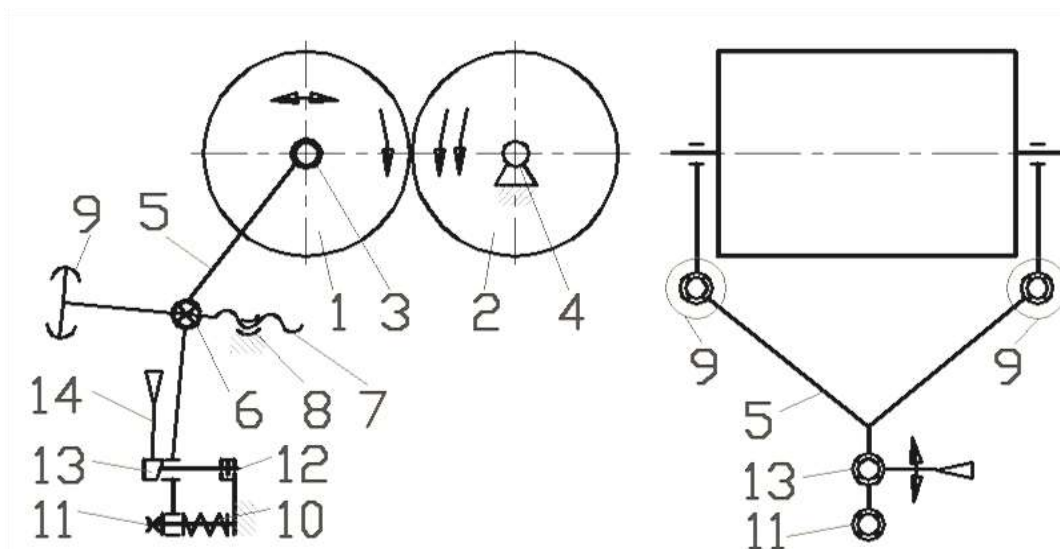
Схема установчого механізму вальцьового верстата.
